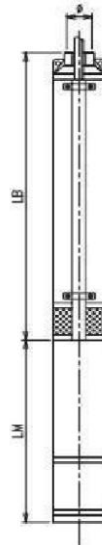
Desenho esquemático dos principais componentes de uma bomba centrífuga.
